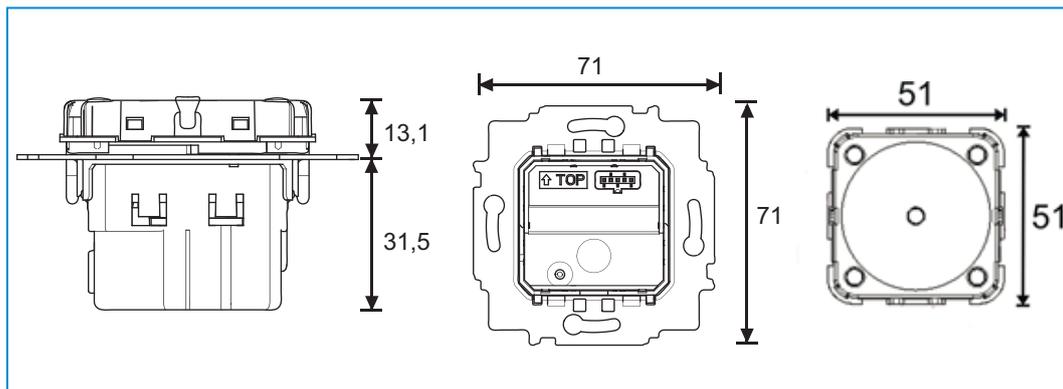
Dimensioni di tutti i tipi di apparecchi descritti
